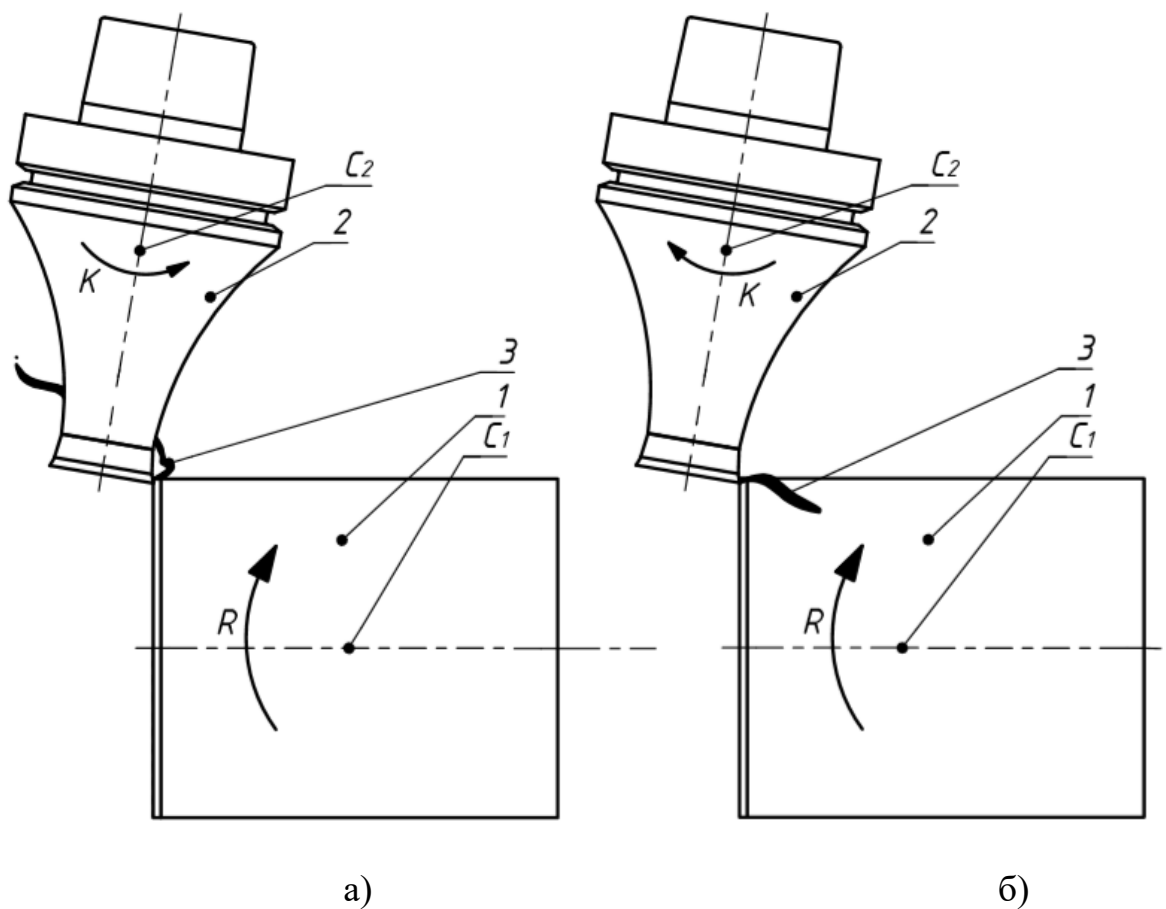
Схема обробки: а - пряме обертання, б - обернене обертання
